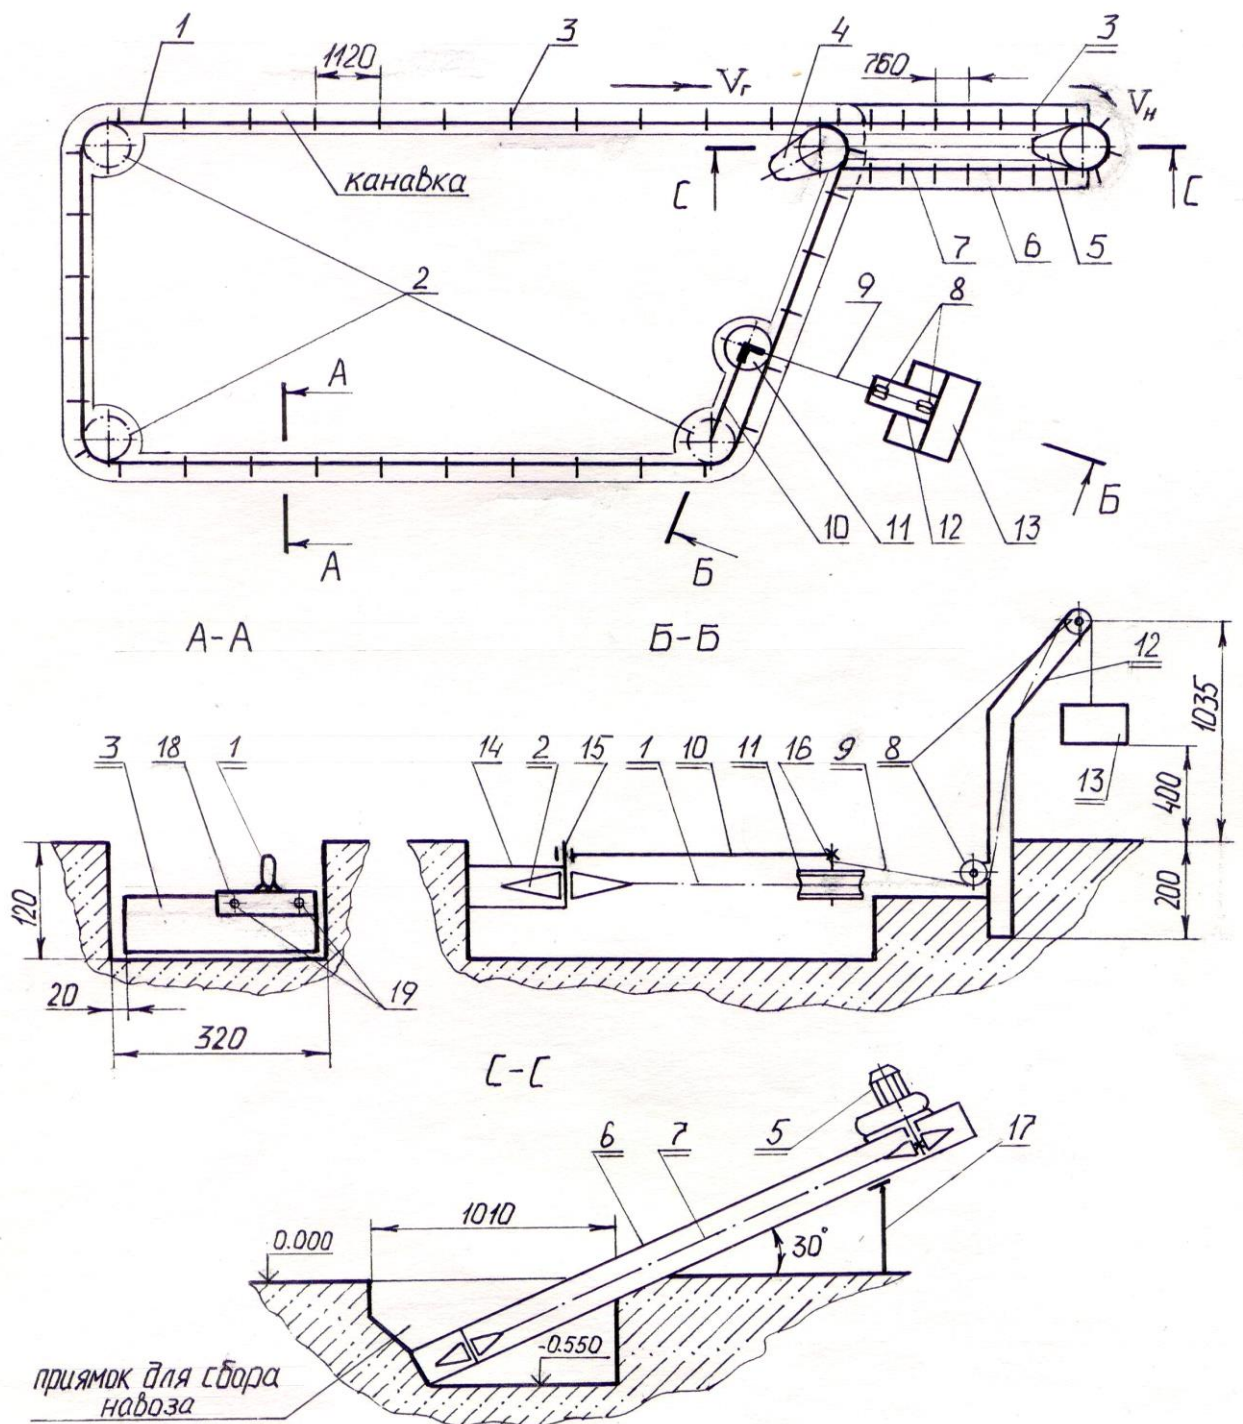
Схема транспортера ТСН-160А для уборки навозной массы
